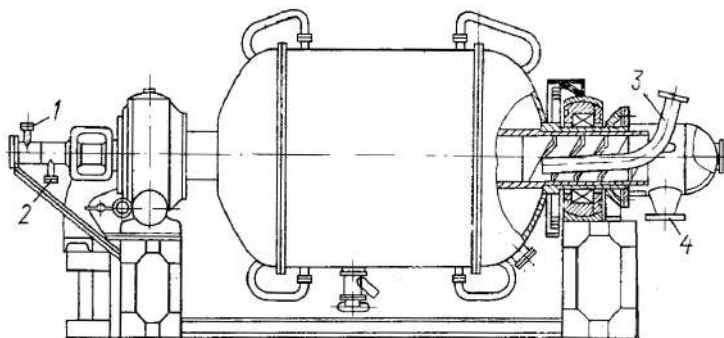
Барабанная вакуумная сушилка типа ВВС с вращающимся корпусом: 1 – штуцер для подвода пара; 2 – штуцер для отвода конденсата; 3 – патрубок для подсоединения сушилки к вакуум-насосу; 4 – патрубок для выгрузки материала.
